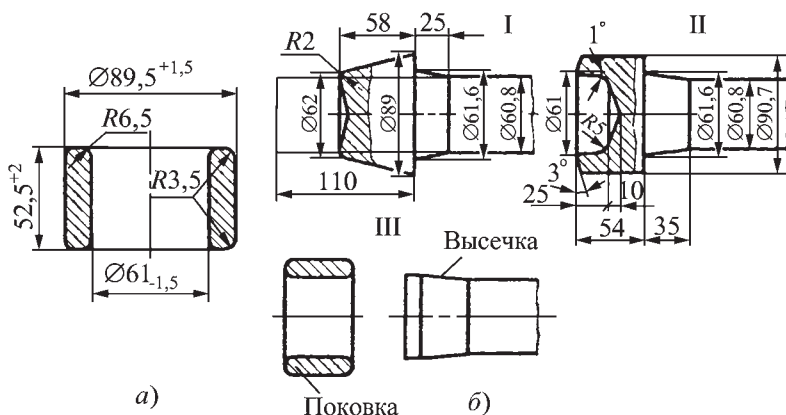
Поковки типа гладкого цилиндрического кольца:
